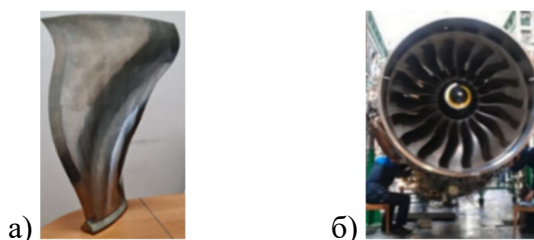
Полая широкохордная рабочая лопатка вентилятора (а) и сборка двигателя-демонстратора ПД-14 в ПАО «Авиадвигатель».
